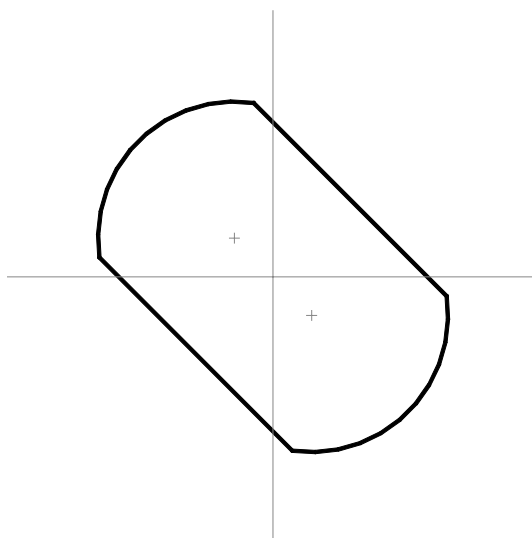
Geometria 3 utilizada para teste do sistema
